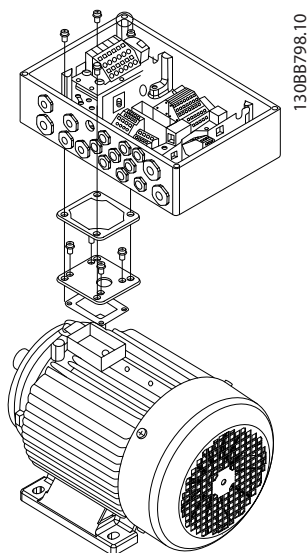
Motormontage des FCD 302 mit Adapterplatte
